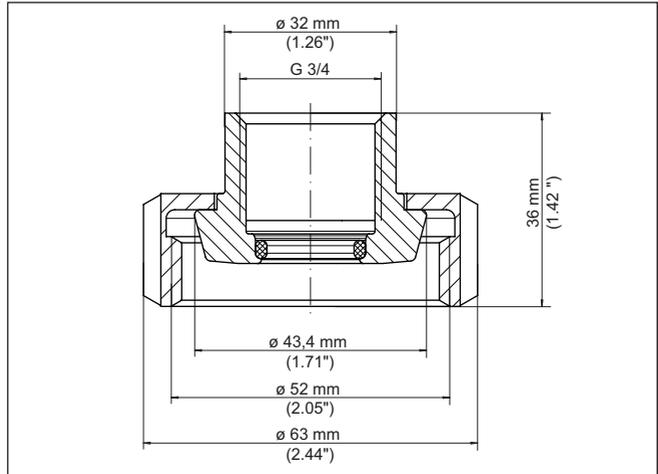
Dimensiones adaptador de rosca G $\frac{3}{4}$ (DIN 3852-X) a racor roscado DN 25 (DIN 11851) PN 25
